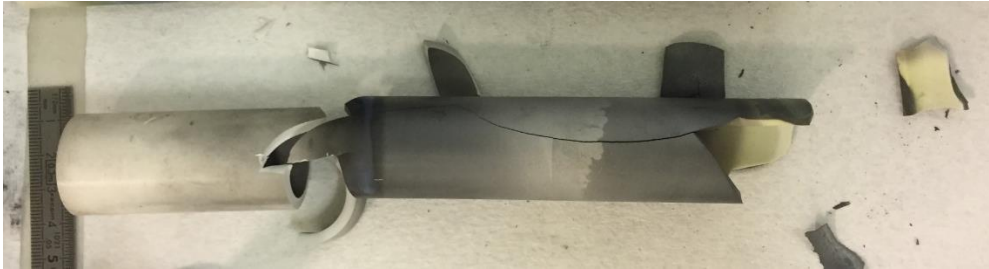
Tube séparateur en zircone Y-FSZ fracturé.
